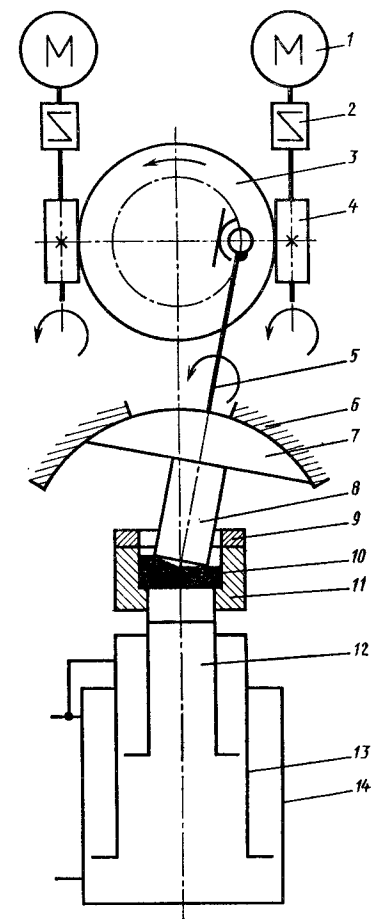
Кинематическая схема машины мод. РХW100А (ПНР) для осадки заготовок обкатыванием:
